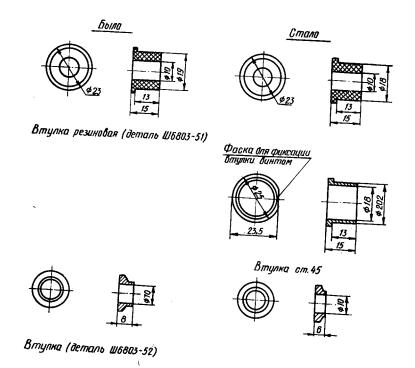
Доработка втулок Ш6003-51, Ш6803-52 и введение дополнительной стальной втулки (Ст. 45) в случае выработки корпуса всасывающего патрубка втулками Ш6803-51
